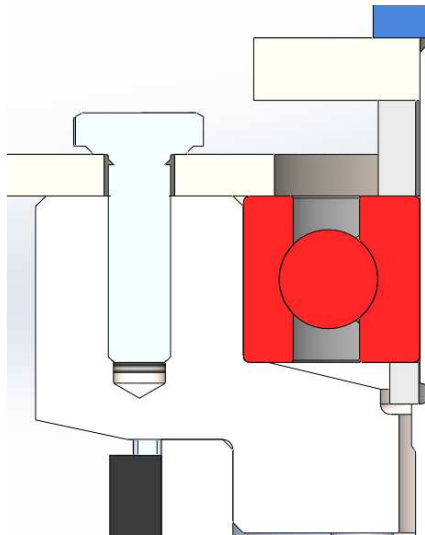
Posicionament axial del conjunt mà (Font pròpia)
